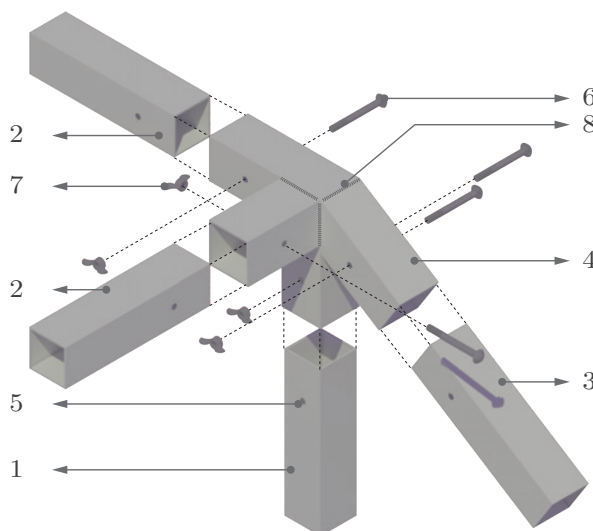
Detalle de la conexión entre cubierta plana a inclinada de 4 vías (3 a 90° y 1 a 32.50°) del habitáculo Modular Emergency Plant. Fuente y elaboración: Autores.
